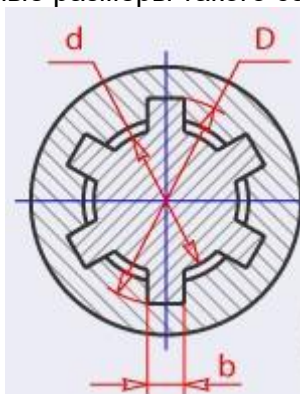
Основные размеры шлицевого прямобоочного соединения
